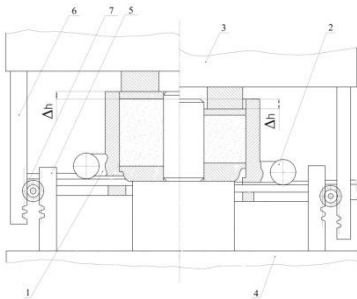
Пресс-форма с зубчатыми рейками:
